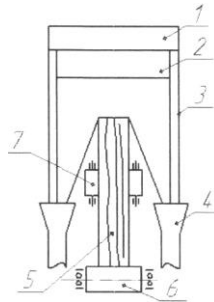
Принципова схема лаконаливної машини для нанесення лаку на крайки меблевих щитів: 1 - лаконаливна головка; 2 - зливна гребля; 3 - напрямні шини; 4 - лійки для лаку; 5 - деталь; 6 - подавальний транспортер; 7 - підтримувальні ролики
